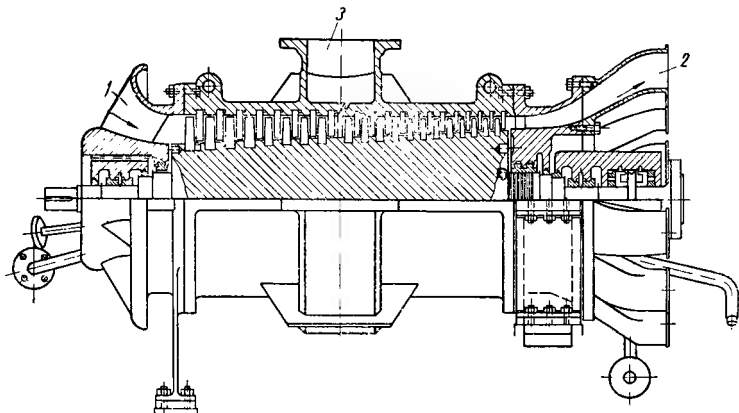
Осевой компрессор с высокой реактивностью дисковой конструкции для реактивного двигателя.
